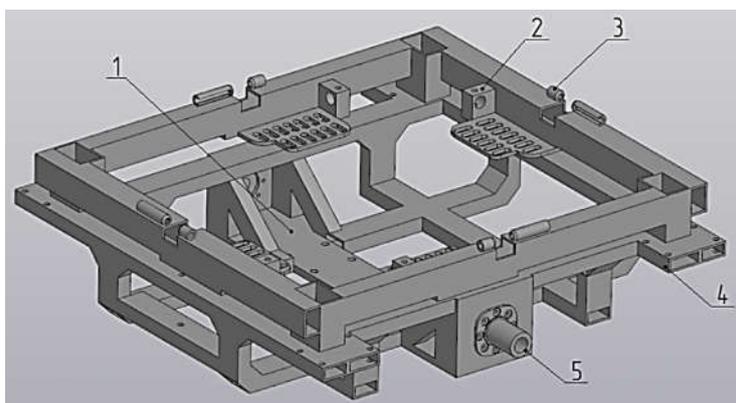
Рама транспортирующей платформы: 1 – площадка для крепления приводов ведущих колес; 2,3 – площадка и ложементы для крепления линейного электропривода управляемой петли механизма разгрузки; 4 – опора крепления рояльного поддерживающего колеса; 5 – ось ведущего колеса
